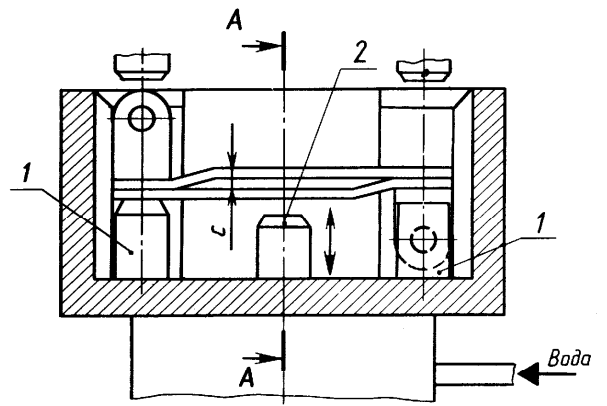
Расположение деталей в ложементе контактной сварочной машины
